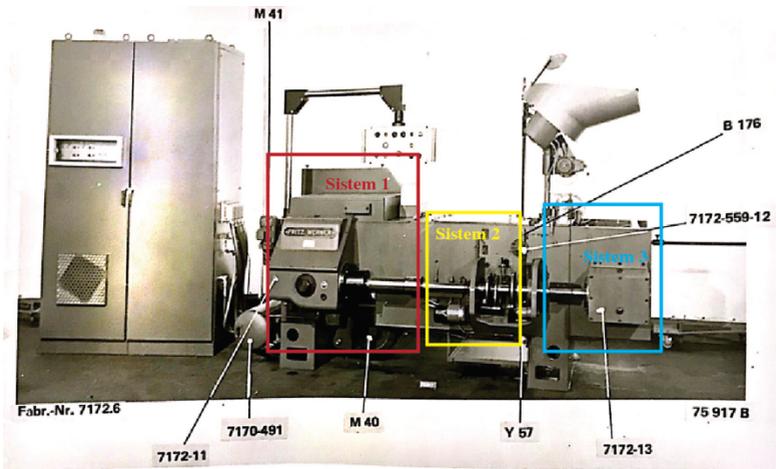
Komponen Cam Sistem Penahan Kerja Aus
